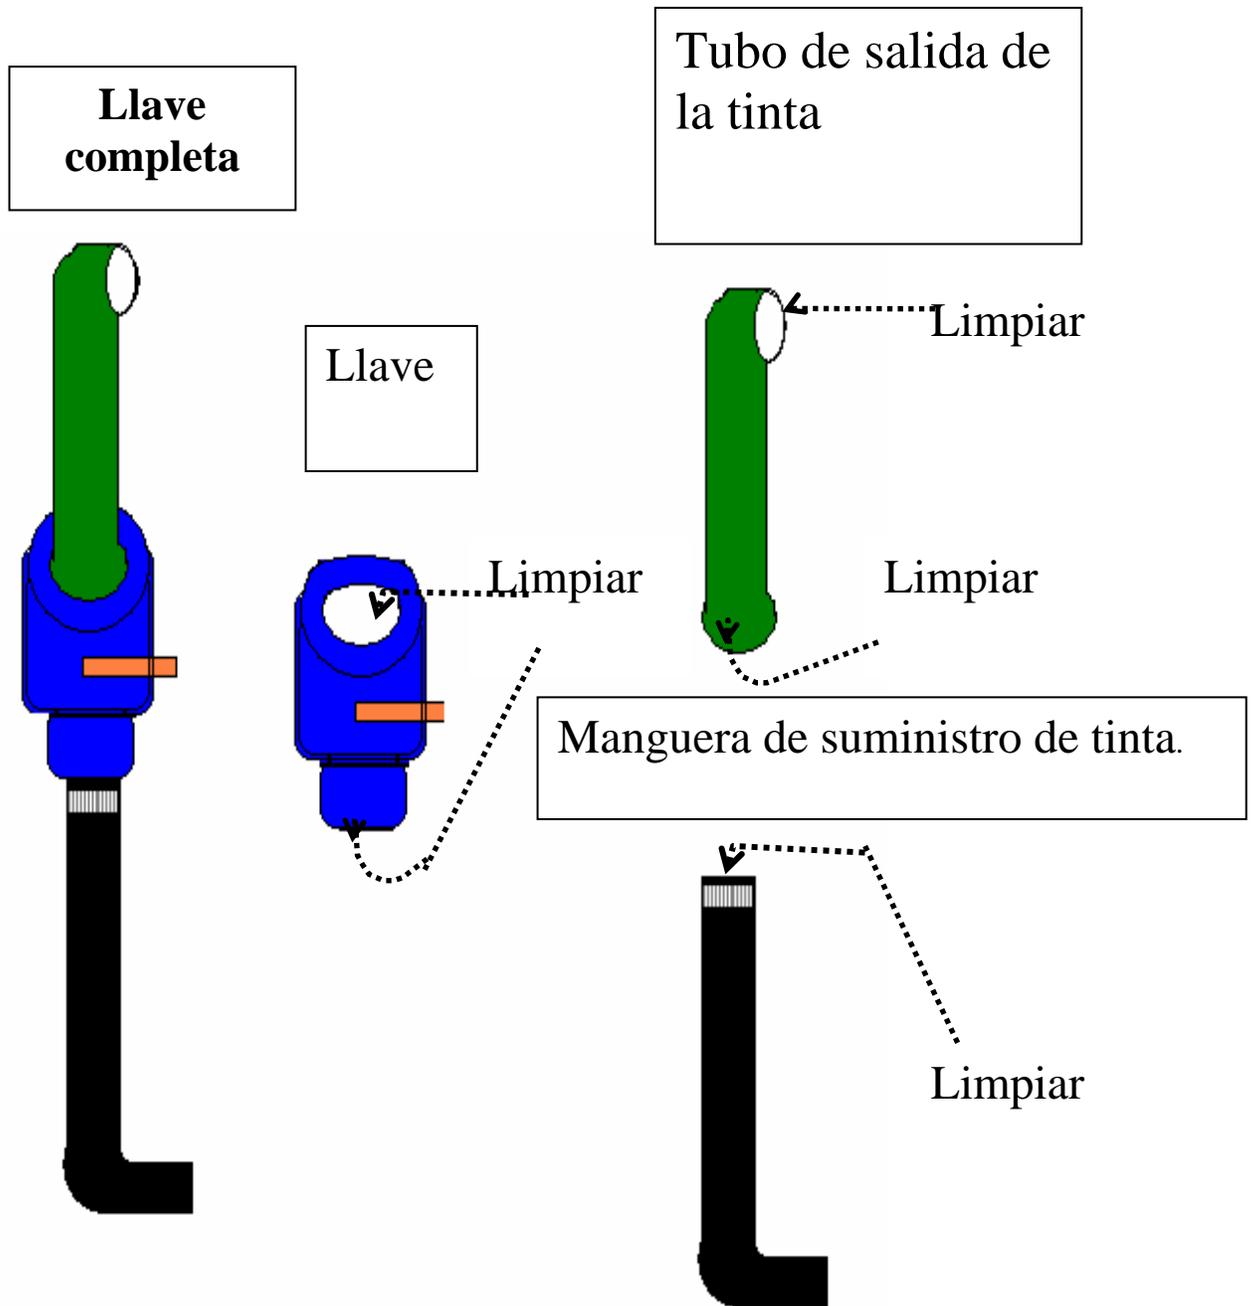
Partes Desensambladas de una Llave Alimentadora de Tinta.
